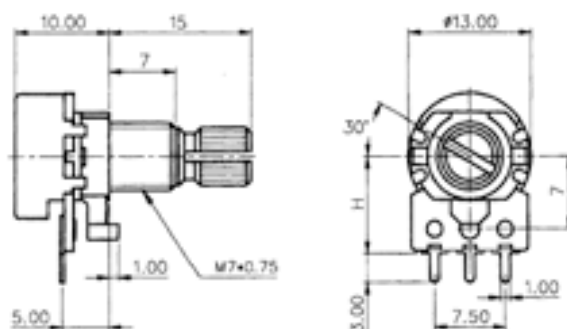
Габаритні розміри змінного резистора 3362P
